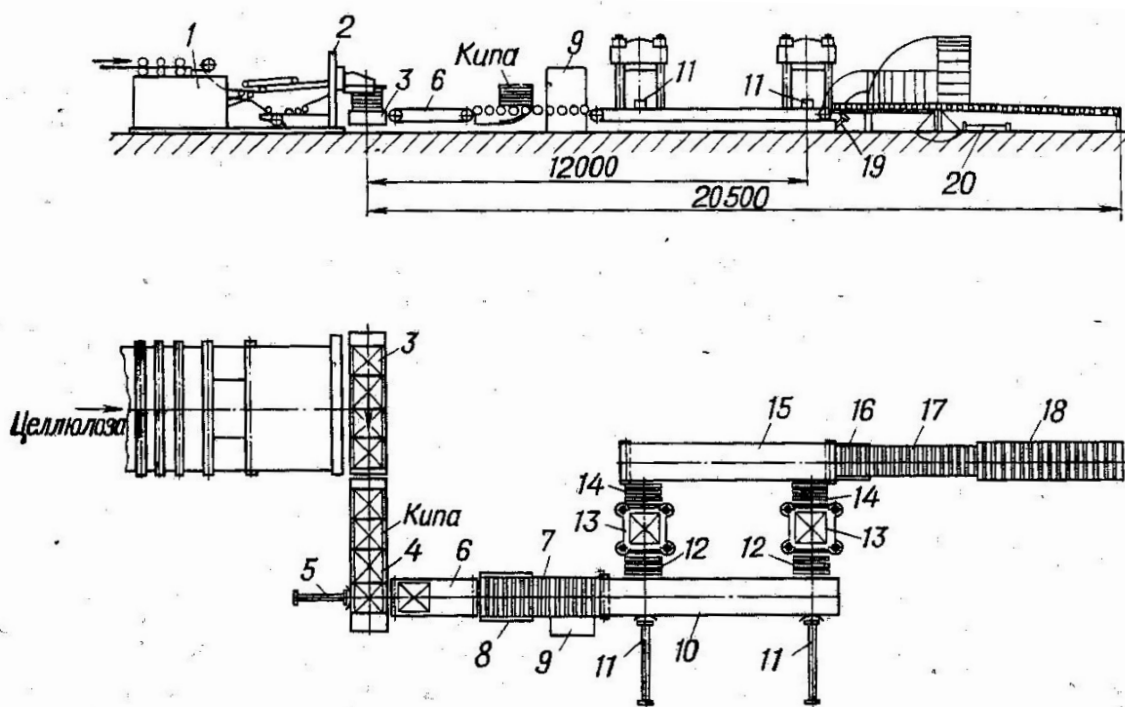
Схема линии упаковки листовой целлюлозы:
